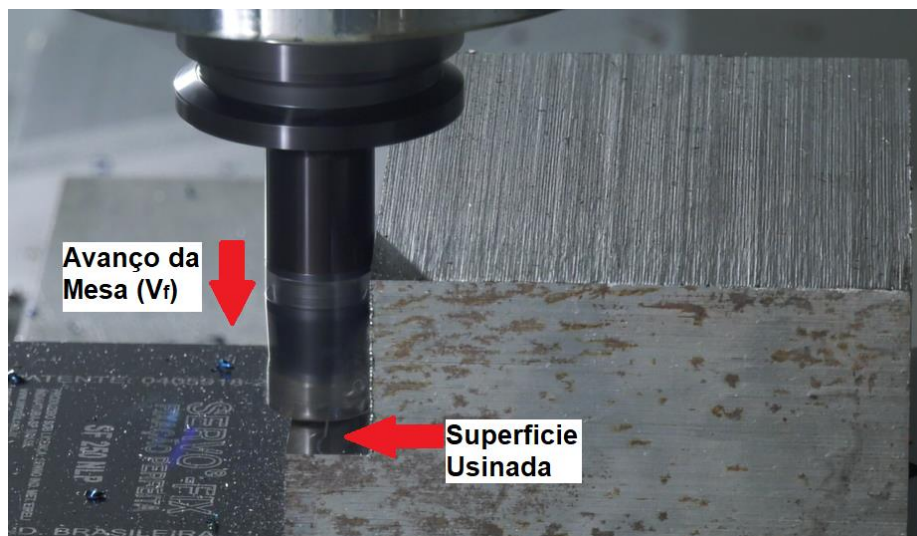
Indicação da superfície usinada e do avanço da mesa, durante fresamento concordante
